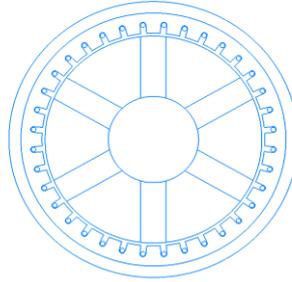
Общий вид электродвигателя с ферритовыми магнитами. Fig. 2. General type of electric motor with ferrite magnets.
